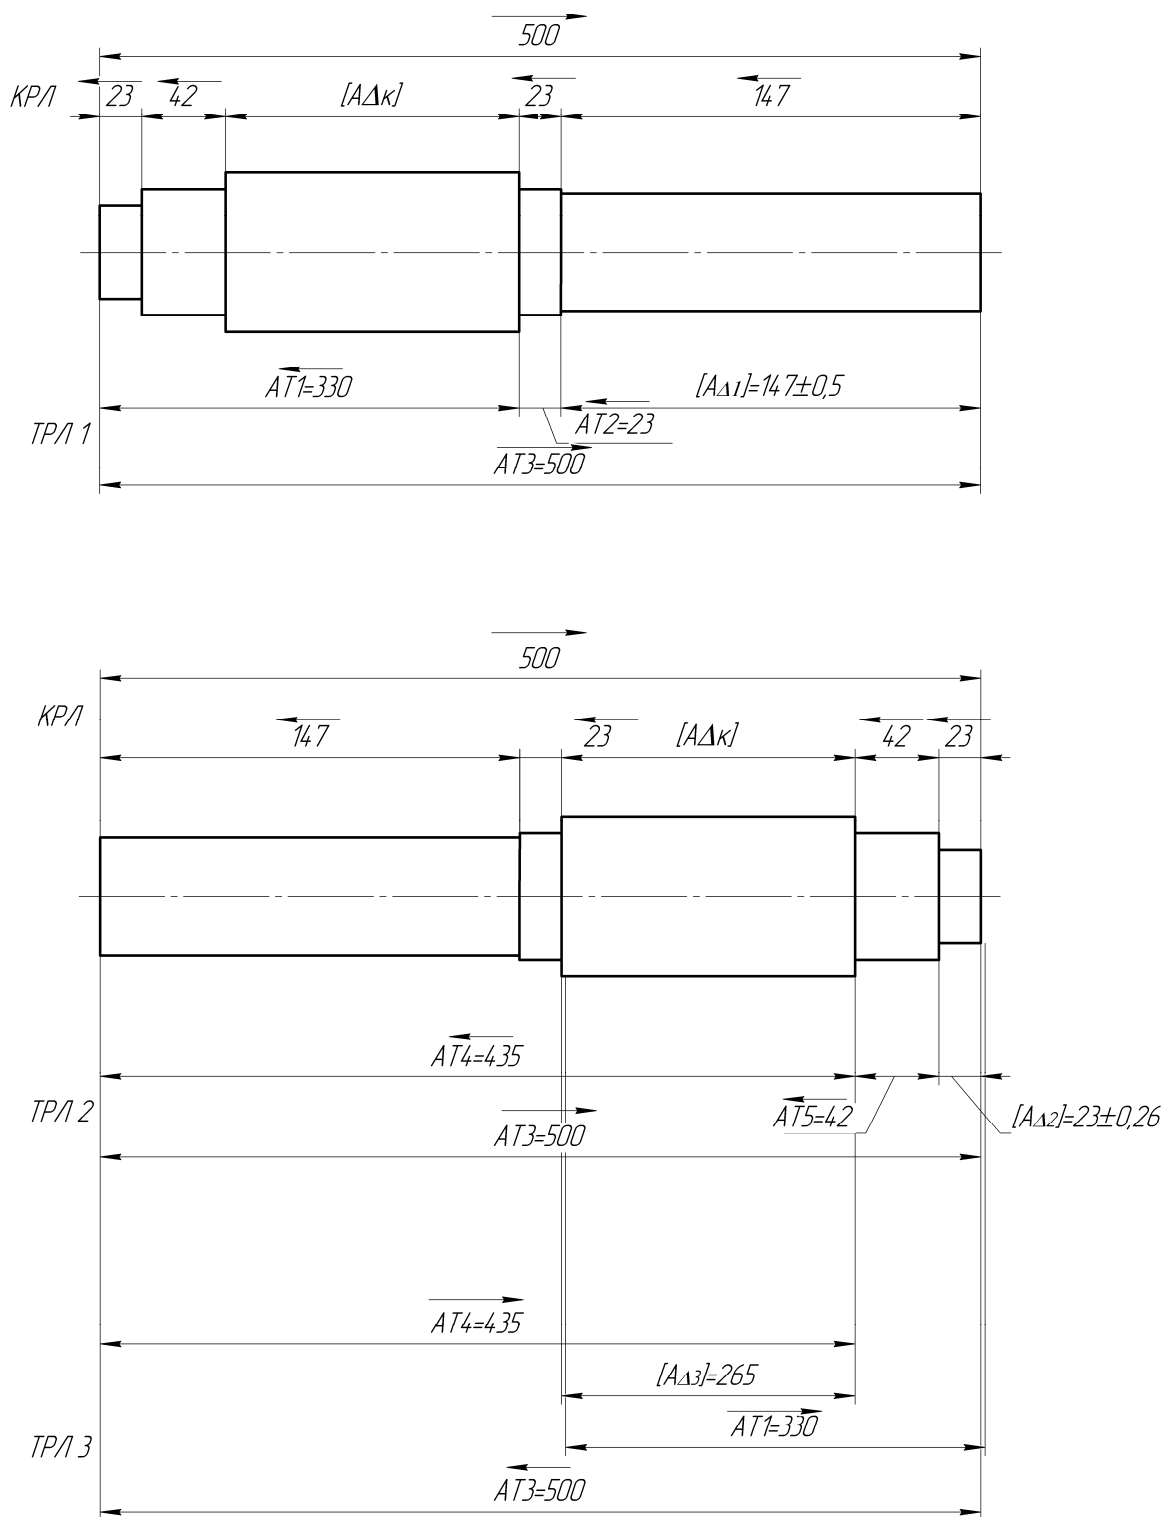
Розрахункові схеми з раціональною розстановкою розмірів для обробки вала
